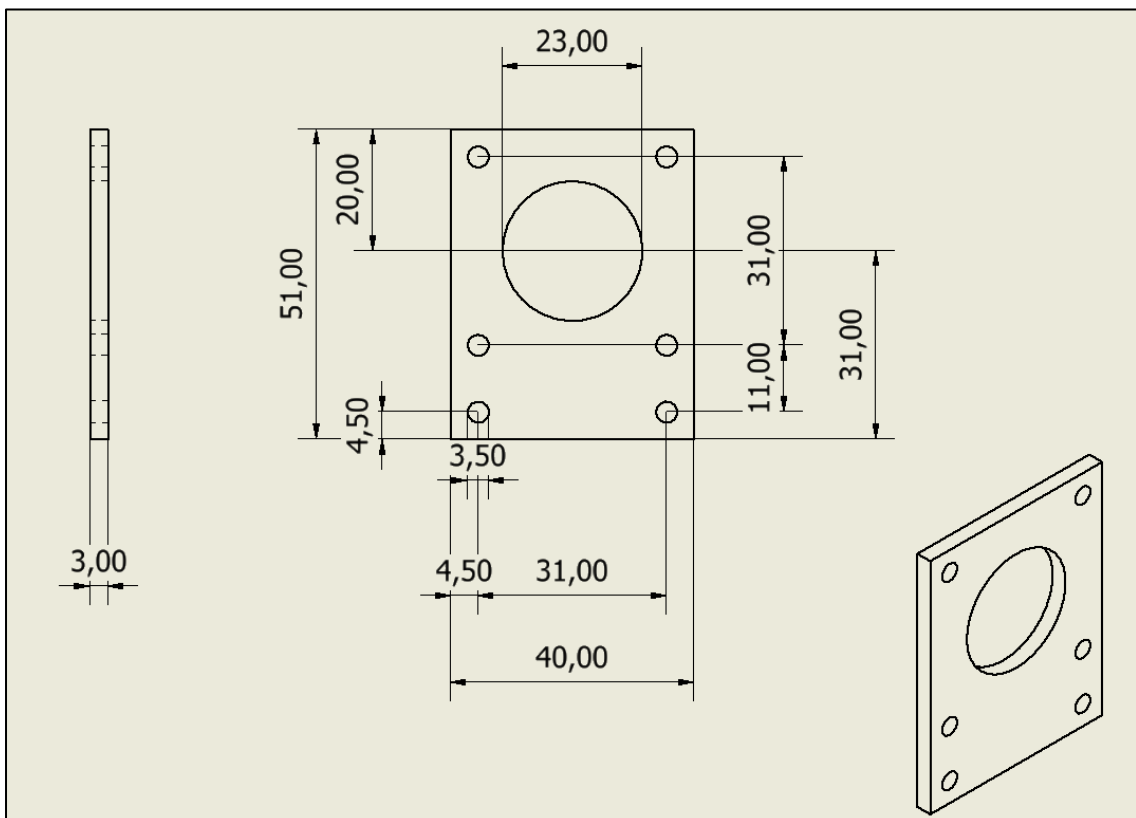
Planos de la pieza para el carro. Elaboración propia.
